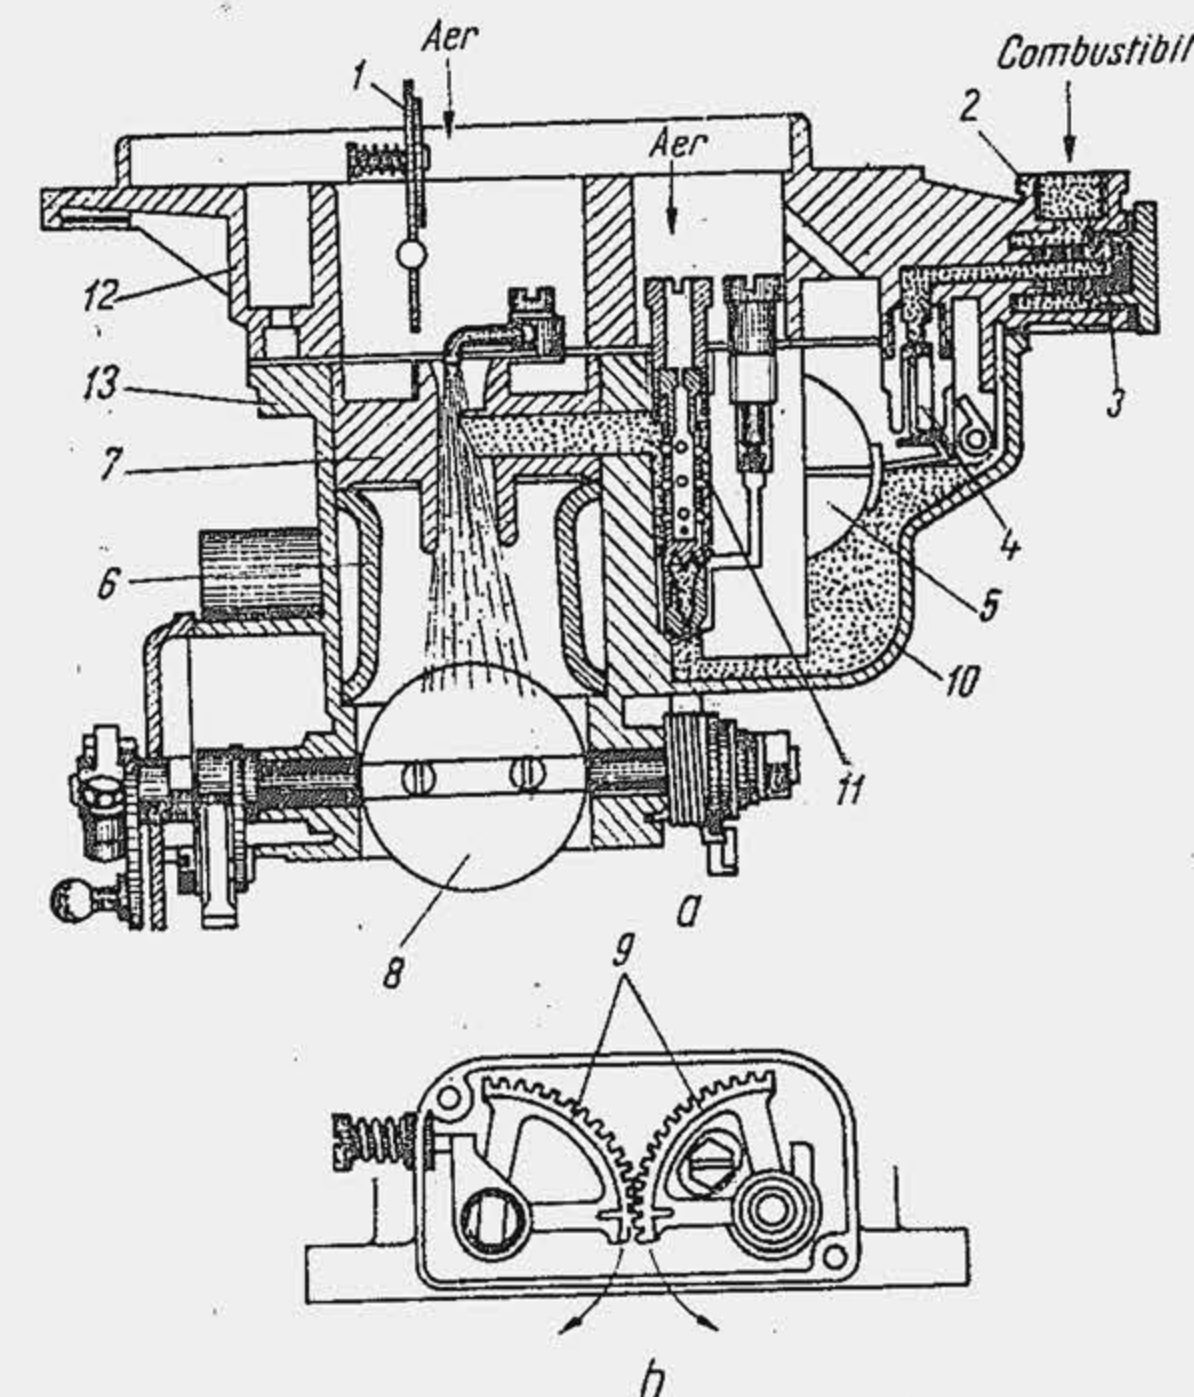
Secțiune prin carburatorul W-211 al motorului SR-211.
